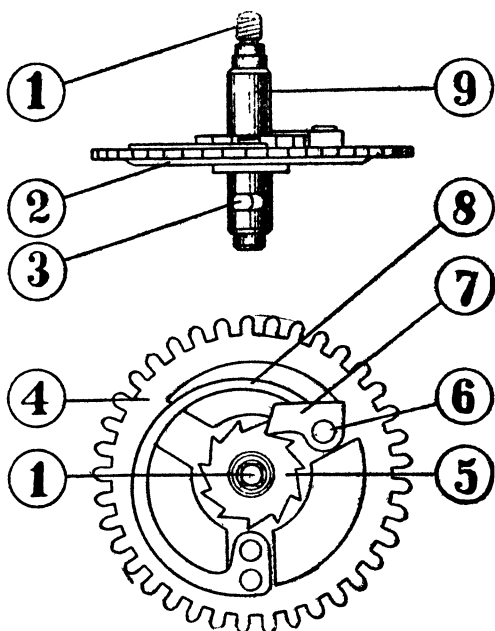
Физейное колесо: 1—резьба для ключа заводки; 2—шайба физейного колеса; 3—крючок для внутреннего витка пружины; 4—физейное колесо; 5—храповое колесо; 6—нипель собачки (шперкегеля); 8—пружинка (шперфедер); 9—ось физейного колеса
